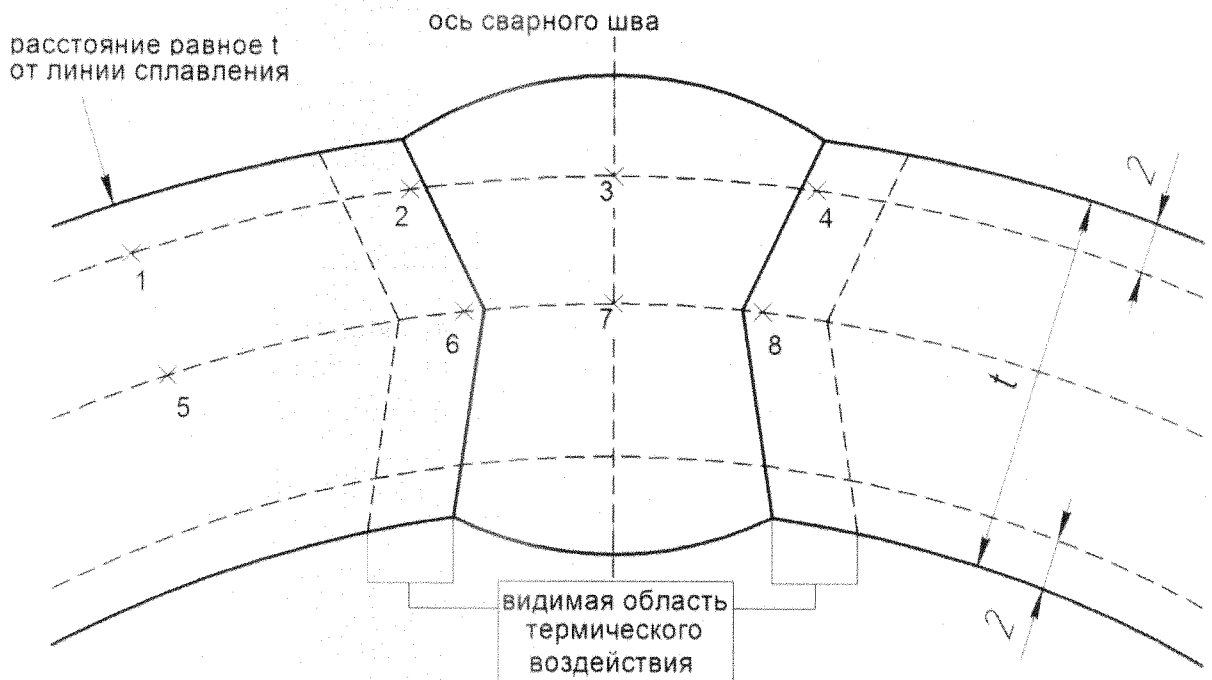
Схема измерения твердости основного металла и сварного соединения труб.
